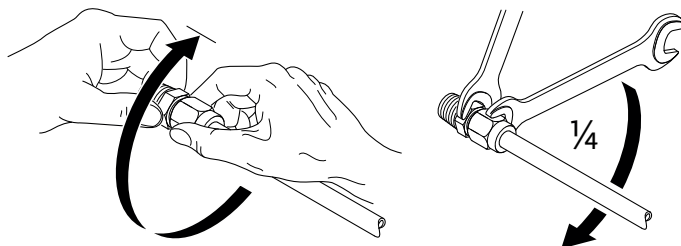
1/4 de rotação adicional da abraçadeira de ligação
